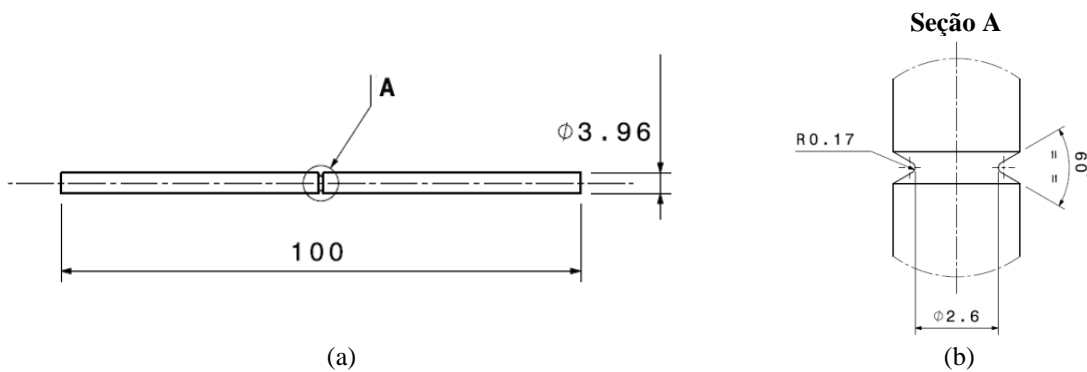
Dimensões em mm do fio com entalhe agudo ($\rho = 0,17 \text{ mm}$) da liga de alumínio 6201-T81. (a) corpo de prova e (b) detalhe do entalhe.
